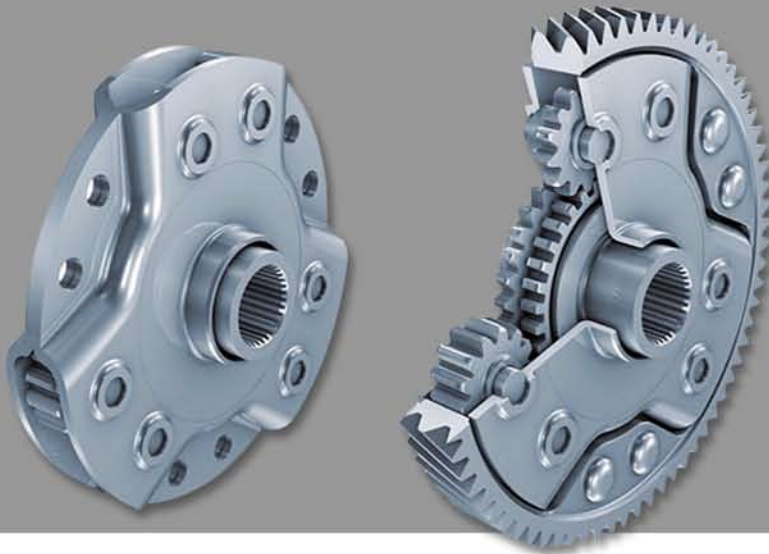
Demonstratorbauteil: kaltumgeformtes Gehäuse eines Ausgleichgetriebes.
